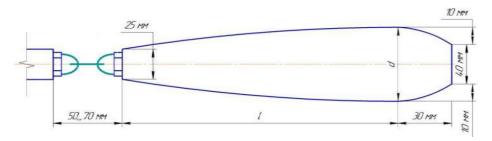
Схема уширителя для кротователя № 2 конусопараболической формы Figure 8 – Scheme of the expander for the mole maker No. 2 of a coneparabolic shape
